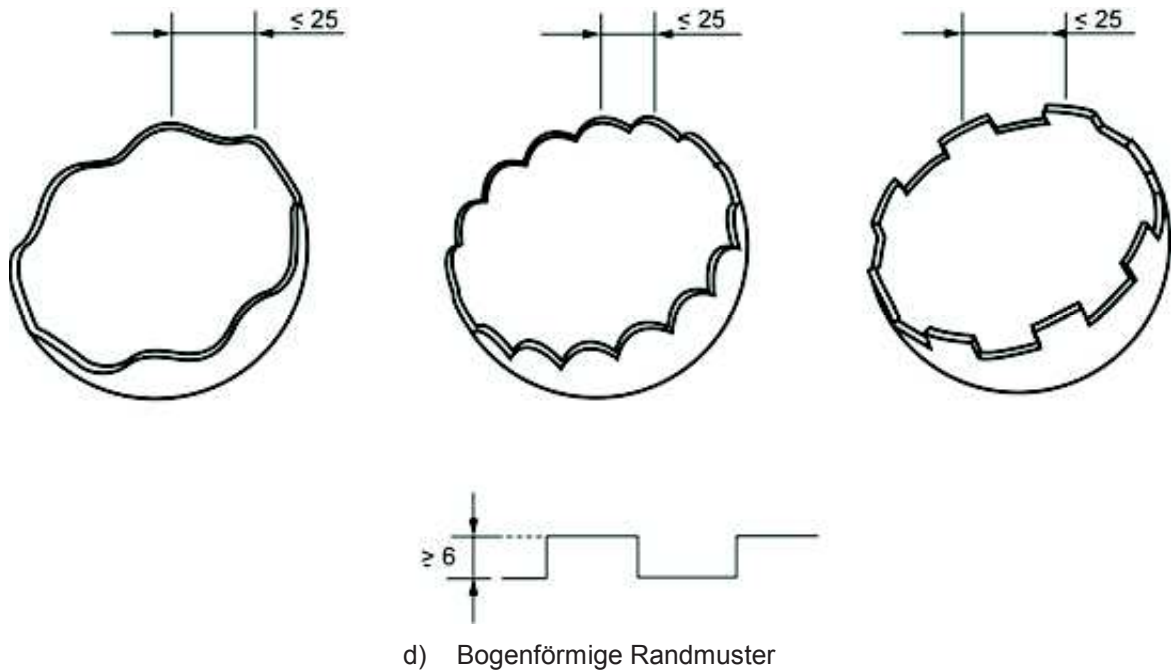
Beispiele für halbkugelförmiges Spielzeug
